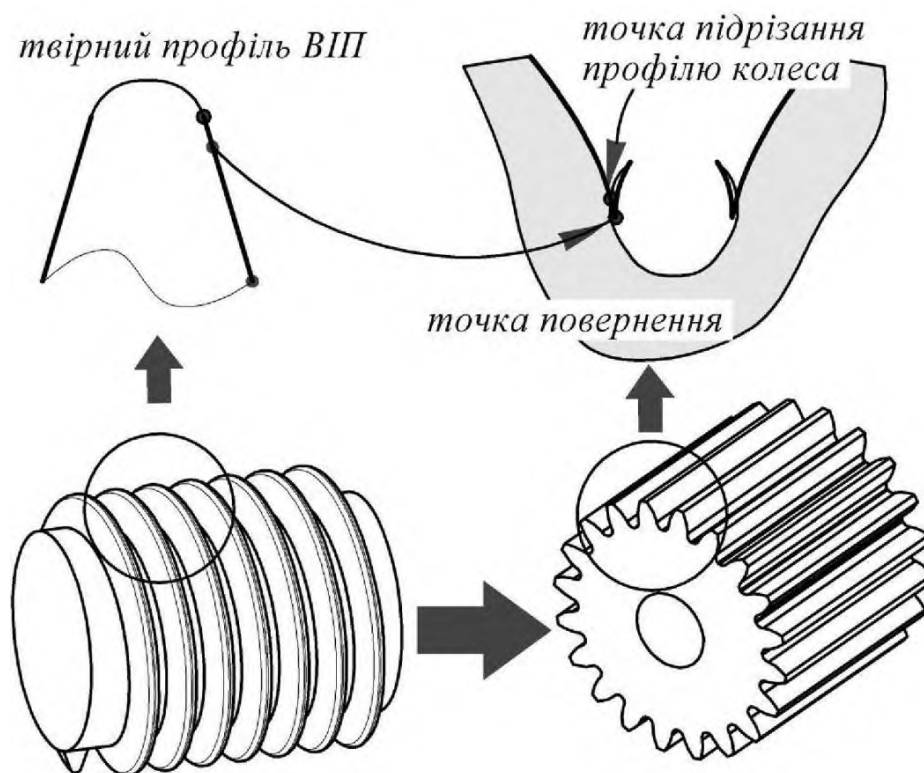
Формування підрізання профілю колеса і точки повернення на ньому
